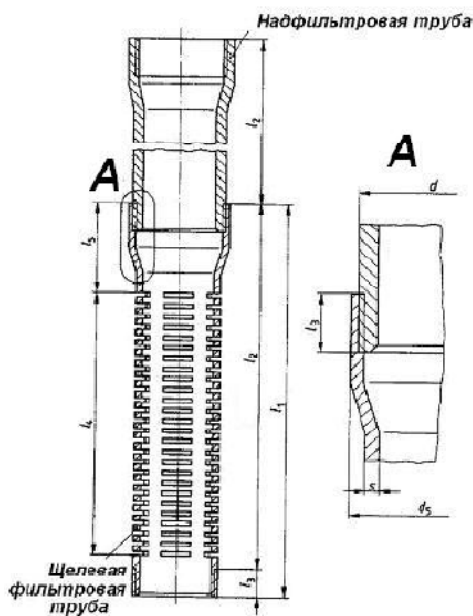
Фильтры трубчатые полимерные со щелевыми отверстиями
